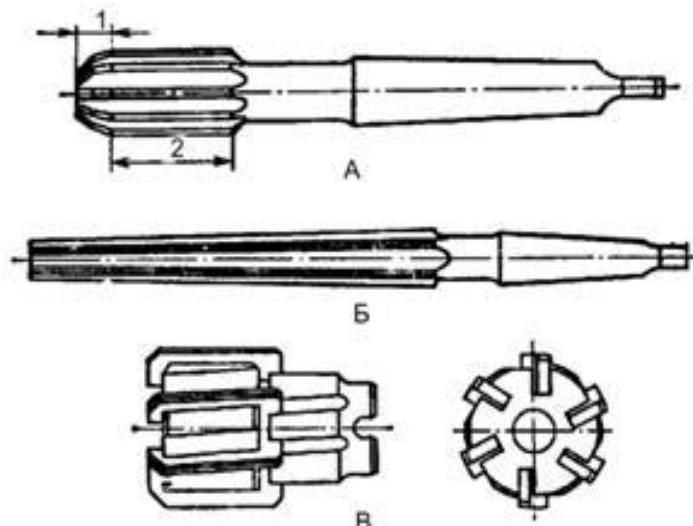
Розгортки: А- циліндрична; Б конічна; В- машинна насадна
